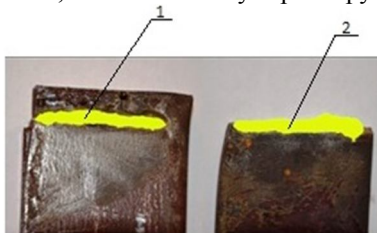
Вид поверхностей разрушения сварного шва:
